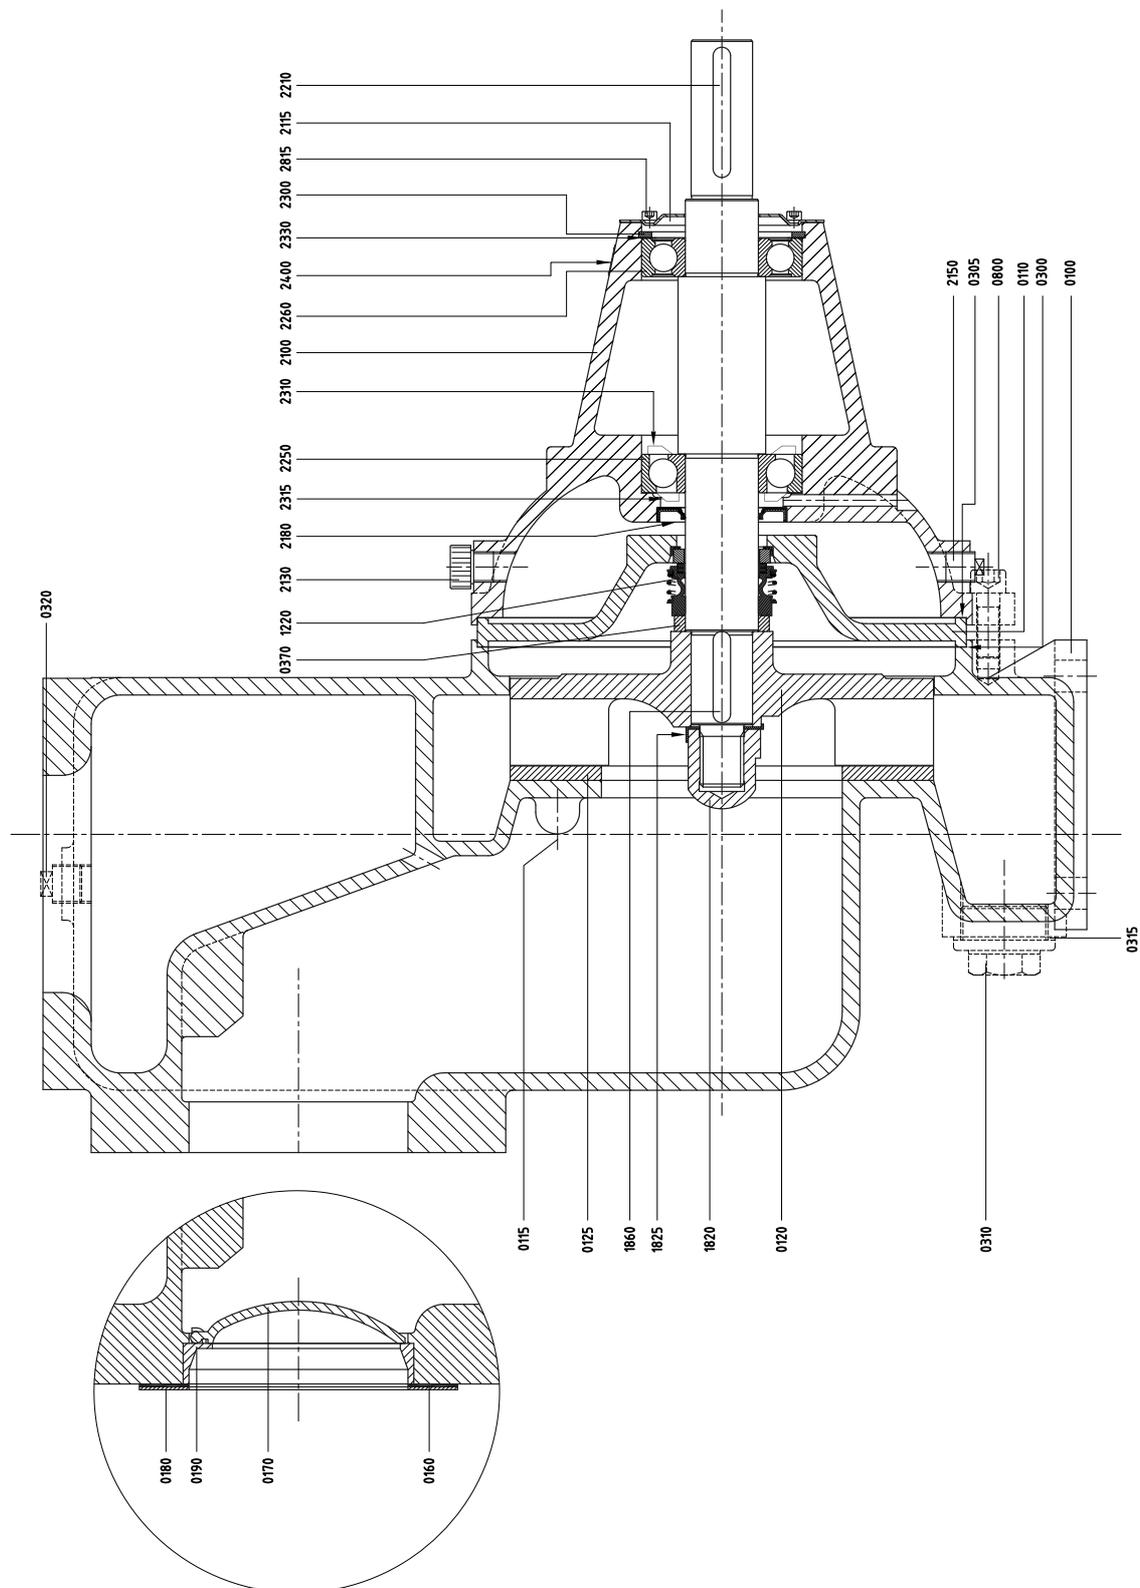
Plan en coupe FRE 150-290b et 150-290.
